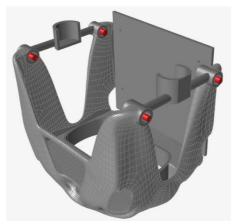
Готовая оптимизированная твердотельная модель детали «Корпус»
